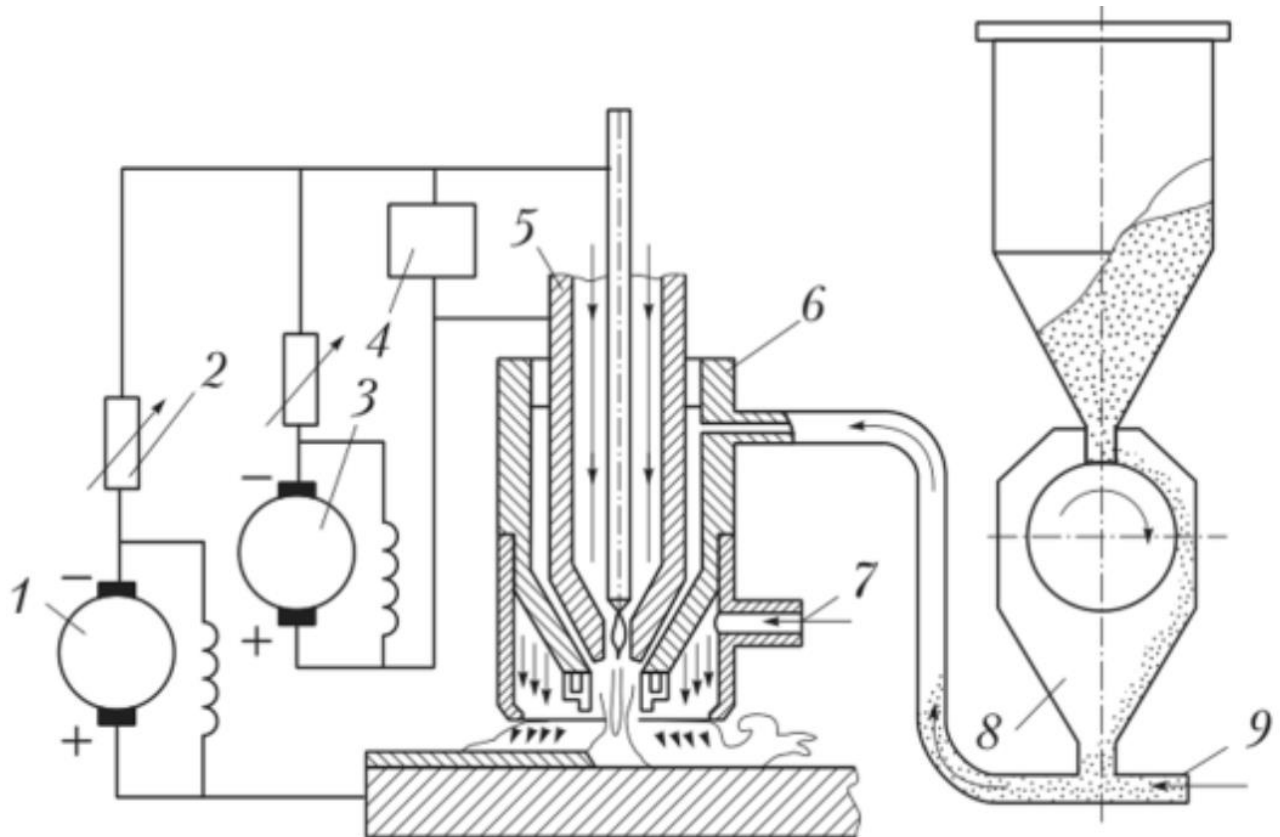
Схема установки для плазмового наплавлення металевим порошком:
